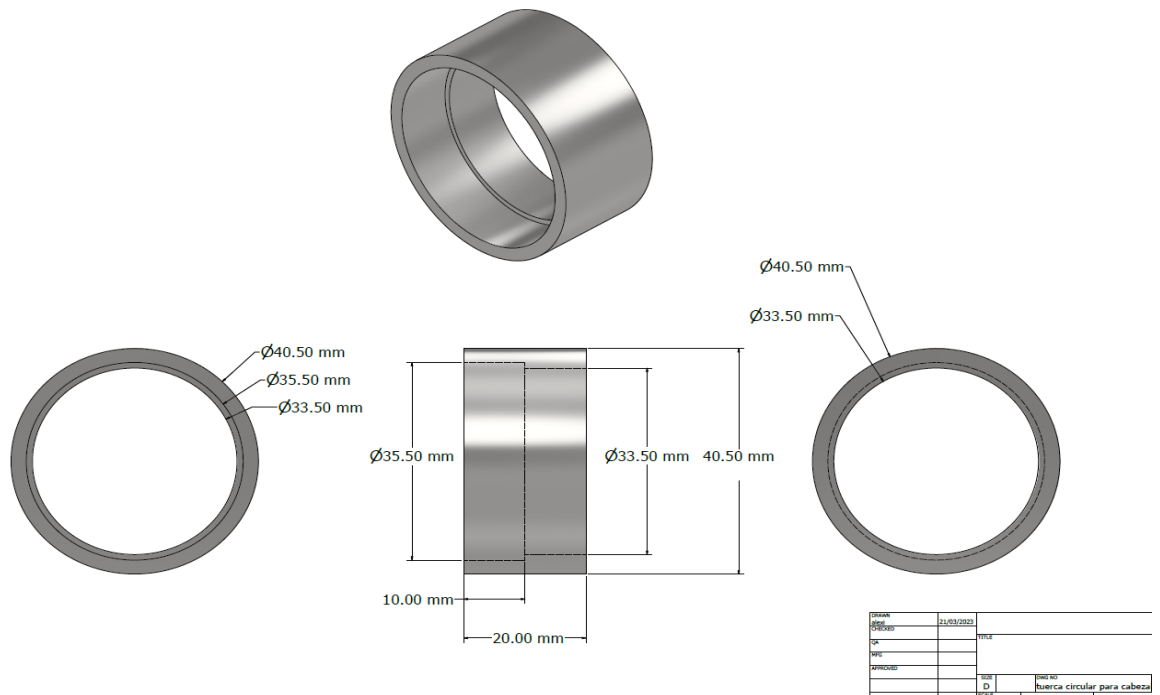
Pieza "B1" de acero que ensambla con pieza "A1".
